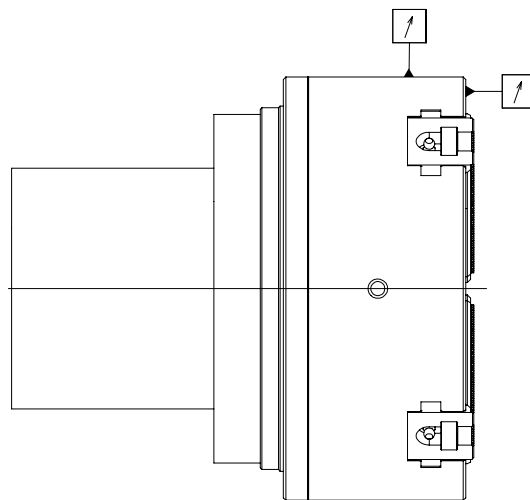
Mandrin de serrage monté sur le faux-plateau
